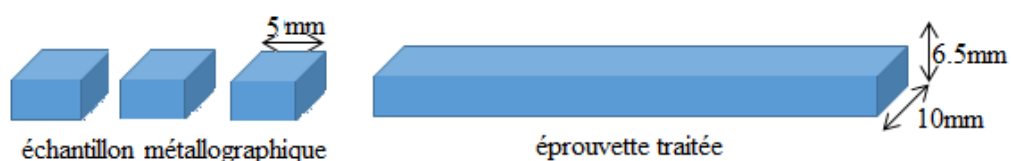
Schematisation Des Eprouvettes Et Dimensions Des Echantillons
